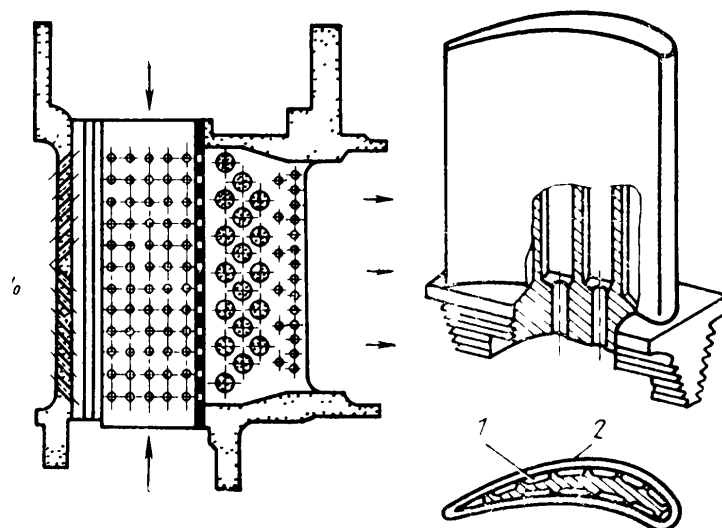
Схема лопатки с пористым охлаждением: 1 - несущий стержень; 2 - оболочка из пористого материала
